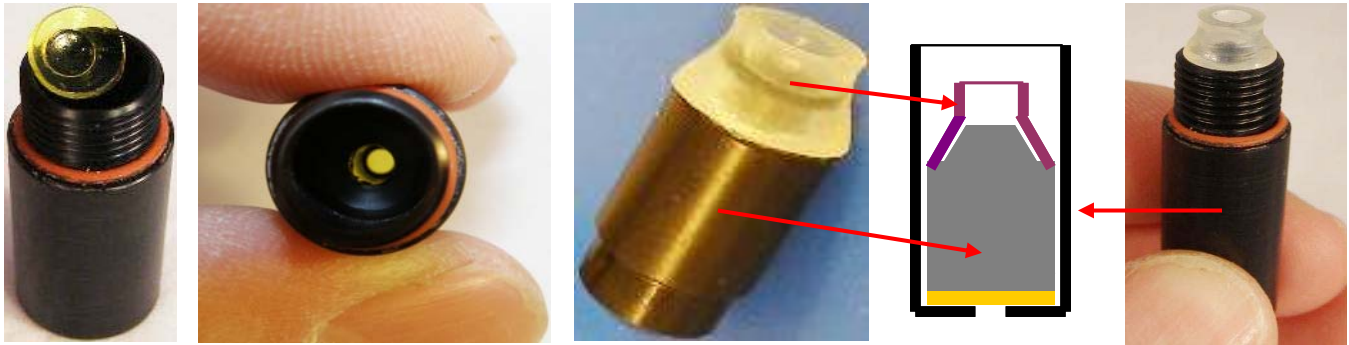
Einsetzen der neuen Membran (Bild 1+2), Membranträger mit Dichtungsring (Bild 3), Systemskizze des eingebauten Membranträgers (Bild 4), Membranträger bevor er in das Membrangehäuse gedrückt wird (Bild 5)
